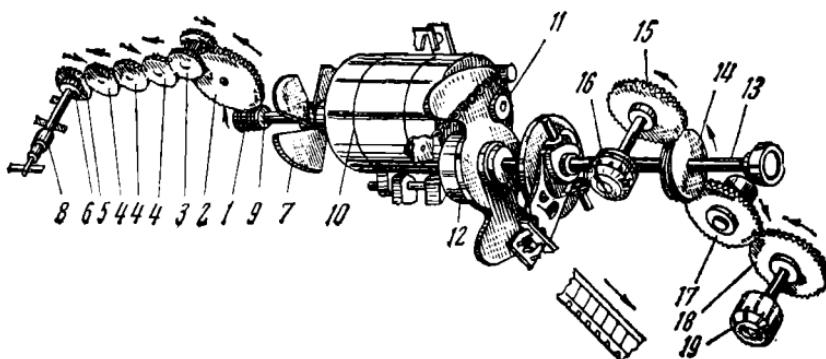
Кинематическая схема кинопроектора ПП-16-4: 1 — червяк; 2 — промежуточная шестерня; 3 — двойная шестерня; 4 — промежуточные шестерни; 5 — шестерни фрикционов; 6 — фрикцион наматывателя; 7 — вентилятор; 8 — вал наматывателя; 9 — вал электродвигателя; 10 — электродвигатель; 11 — шкив электродвигателя; 12 — шкив обтюратора; 13 — ведущий вал; 14 — червячная шестерня; 15 — шестерня вала тяущего барабана; 16 — тяущий барабан; 17 — промежуточная шестерня; 18 — шестерня вала задерживающего барабана; 19 — задерживающий барабан
